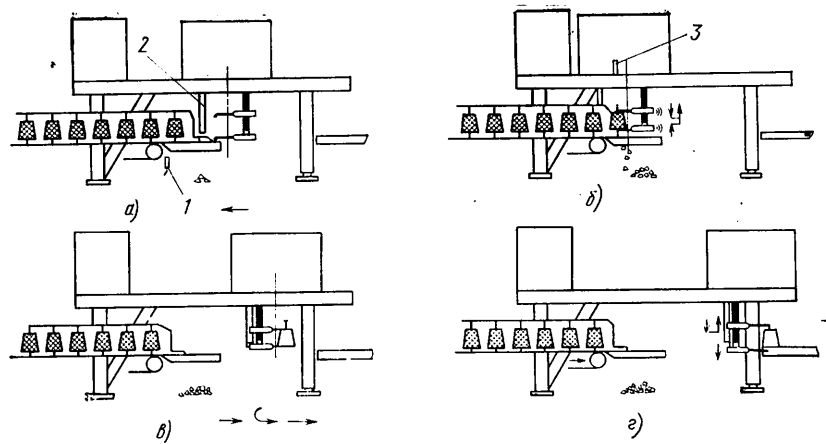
Схема работы робототехнического комплекса для извлечения отливок из открытой формы: а — «поиск» отливки (при помощи датчика 1) и перемещение захвата; б — углубление захвата в форму при помощи вибратора 2 (контроль положения — датчиком 3); в — извлечение отливки (после сигнала от датчика 3), поворот ее на 180° и перемещение на дальнейшую обработку (при перемещении захват может вибрировать); г — контроль охлаждения отливки и передача ее на выбивную решетку при помощи поворотного стола или транспортера
